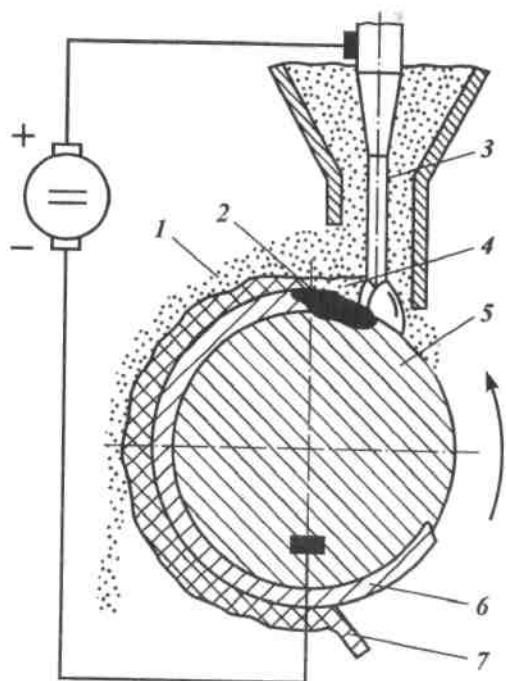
Схема наплавки под слоем флюса: 1- нерасплавленный флюс; 2- жидкий металл; 3 -электрод; 4 - расплавленный шлак; 5 - деталь; 6 - наплавляемый металл; 7 - шлаковая корка
